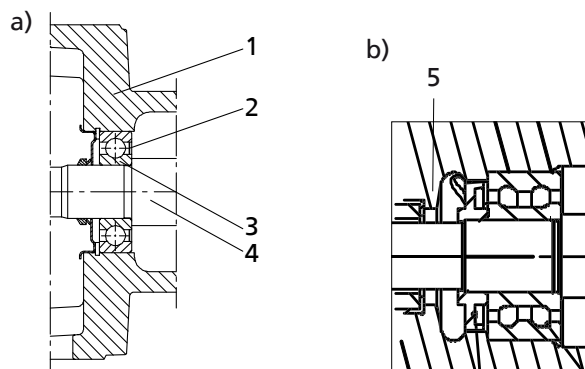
Установка радиального шарикоподшипника а) узел вала 25 и 35 б) узел вала 17
